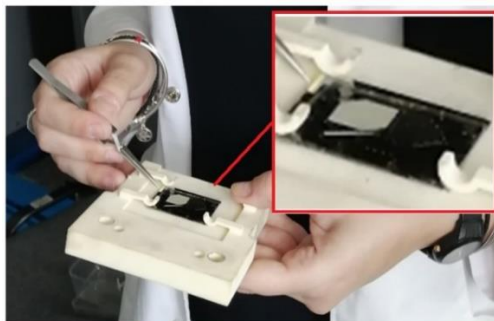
Prinderea dispozitivului în suportul fabricat cu ajutorul tehnologiei 3D printing
